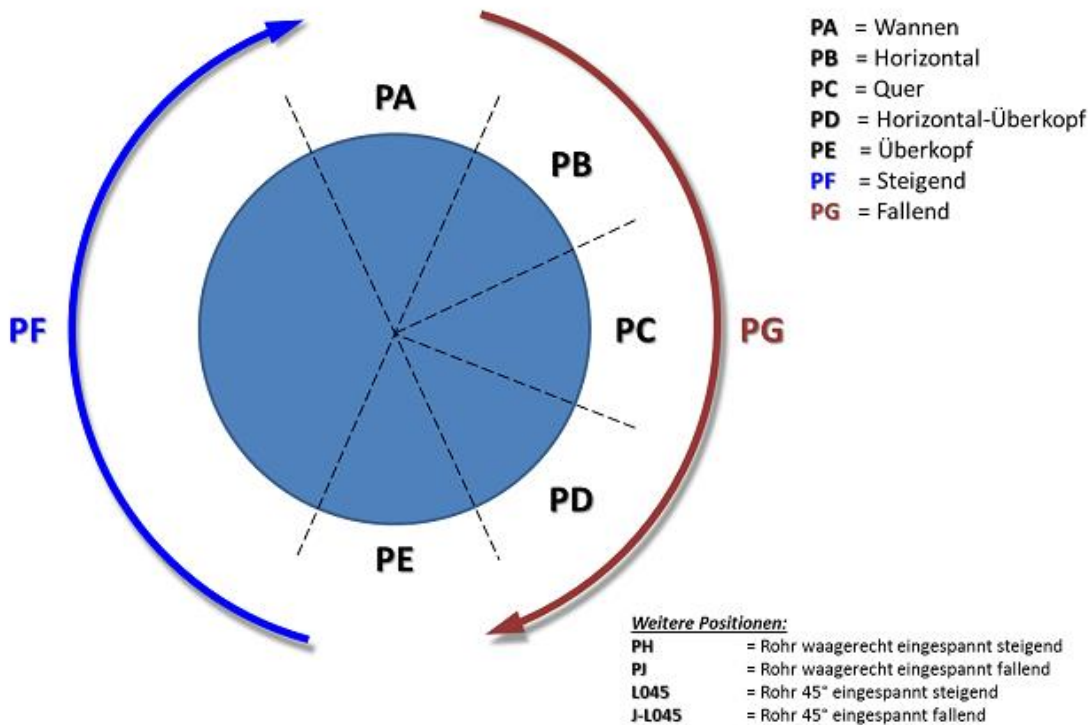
Schweißpositionen nach ISO 9647.
